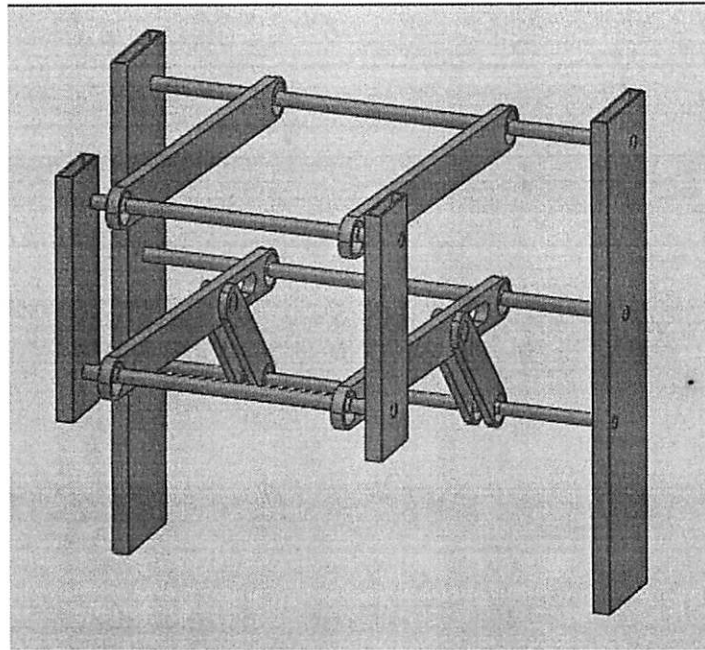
Vista Tridimensional do Mecanismo de Elevação
